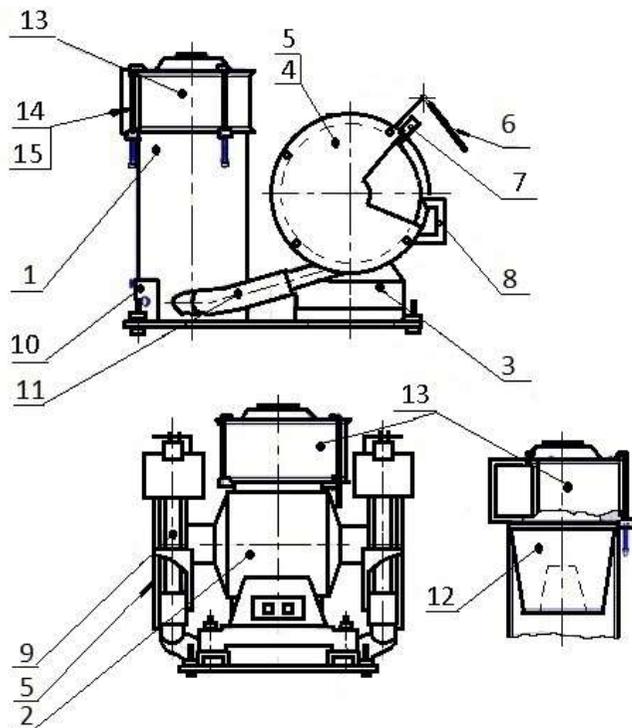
Общий вид заточного станка ЗСВ25 с вытяжкой:
